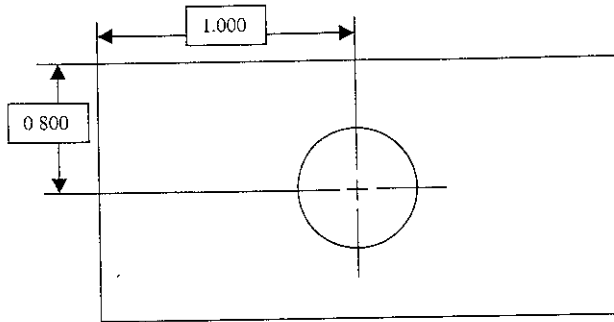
Comp. común para un dibujo con dimensiones y tolerancias geométricas.
